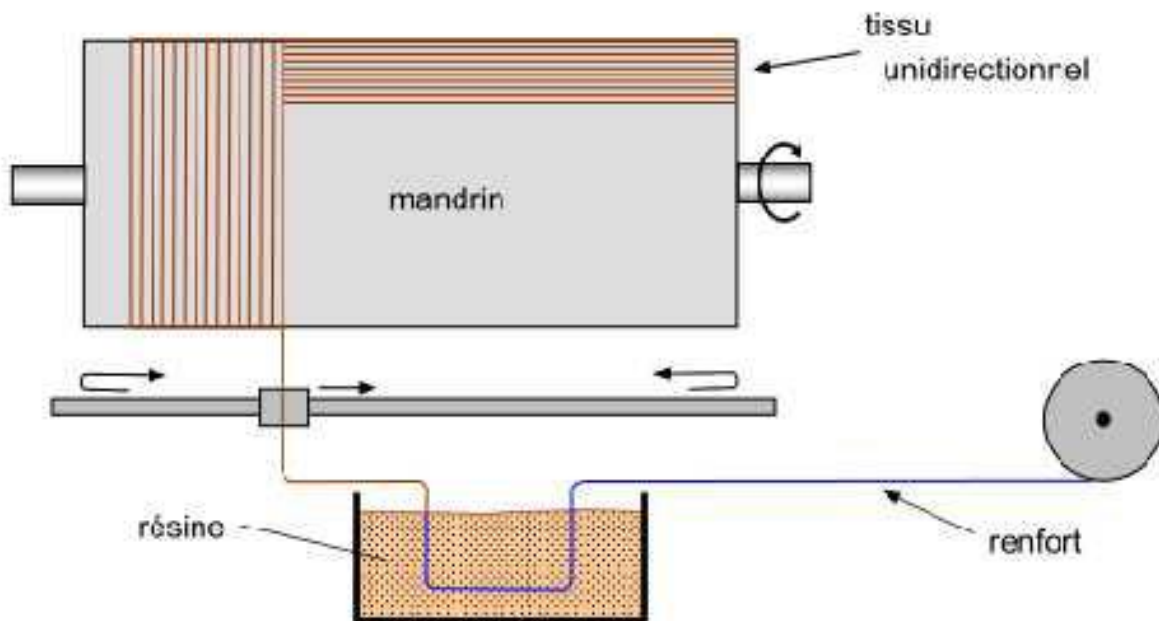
Principe d'enroulement circonférentiel [2].
